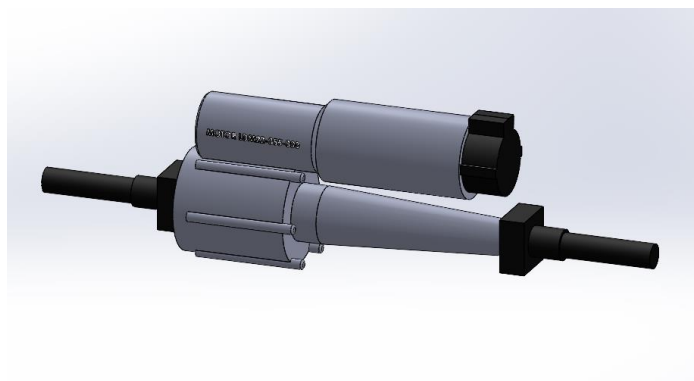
Modelo CAD del Motor LDM22-355-800 [fuente propia]
